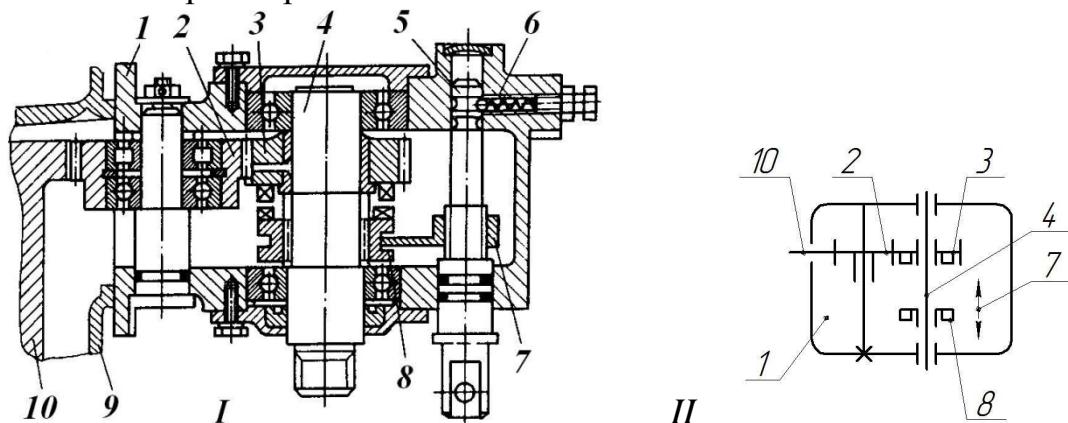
Коробка отбора мощности крана КС-2561Д: I – общий вид, II – кинематическая схема, 1 – корпус, 2, 3 – шестерни, 4 – вал, 5 – валик, 6 – фиксатор, 7 – вилка, 8 – муфта, 9 – коробка передач базового автомобиля, 10 – шестерня
